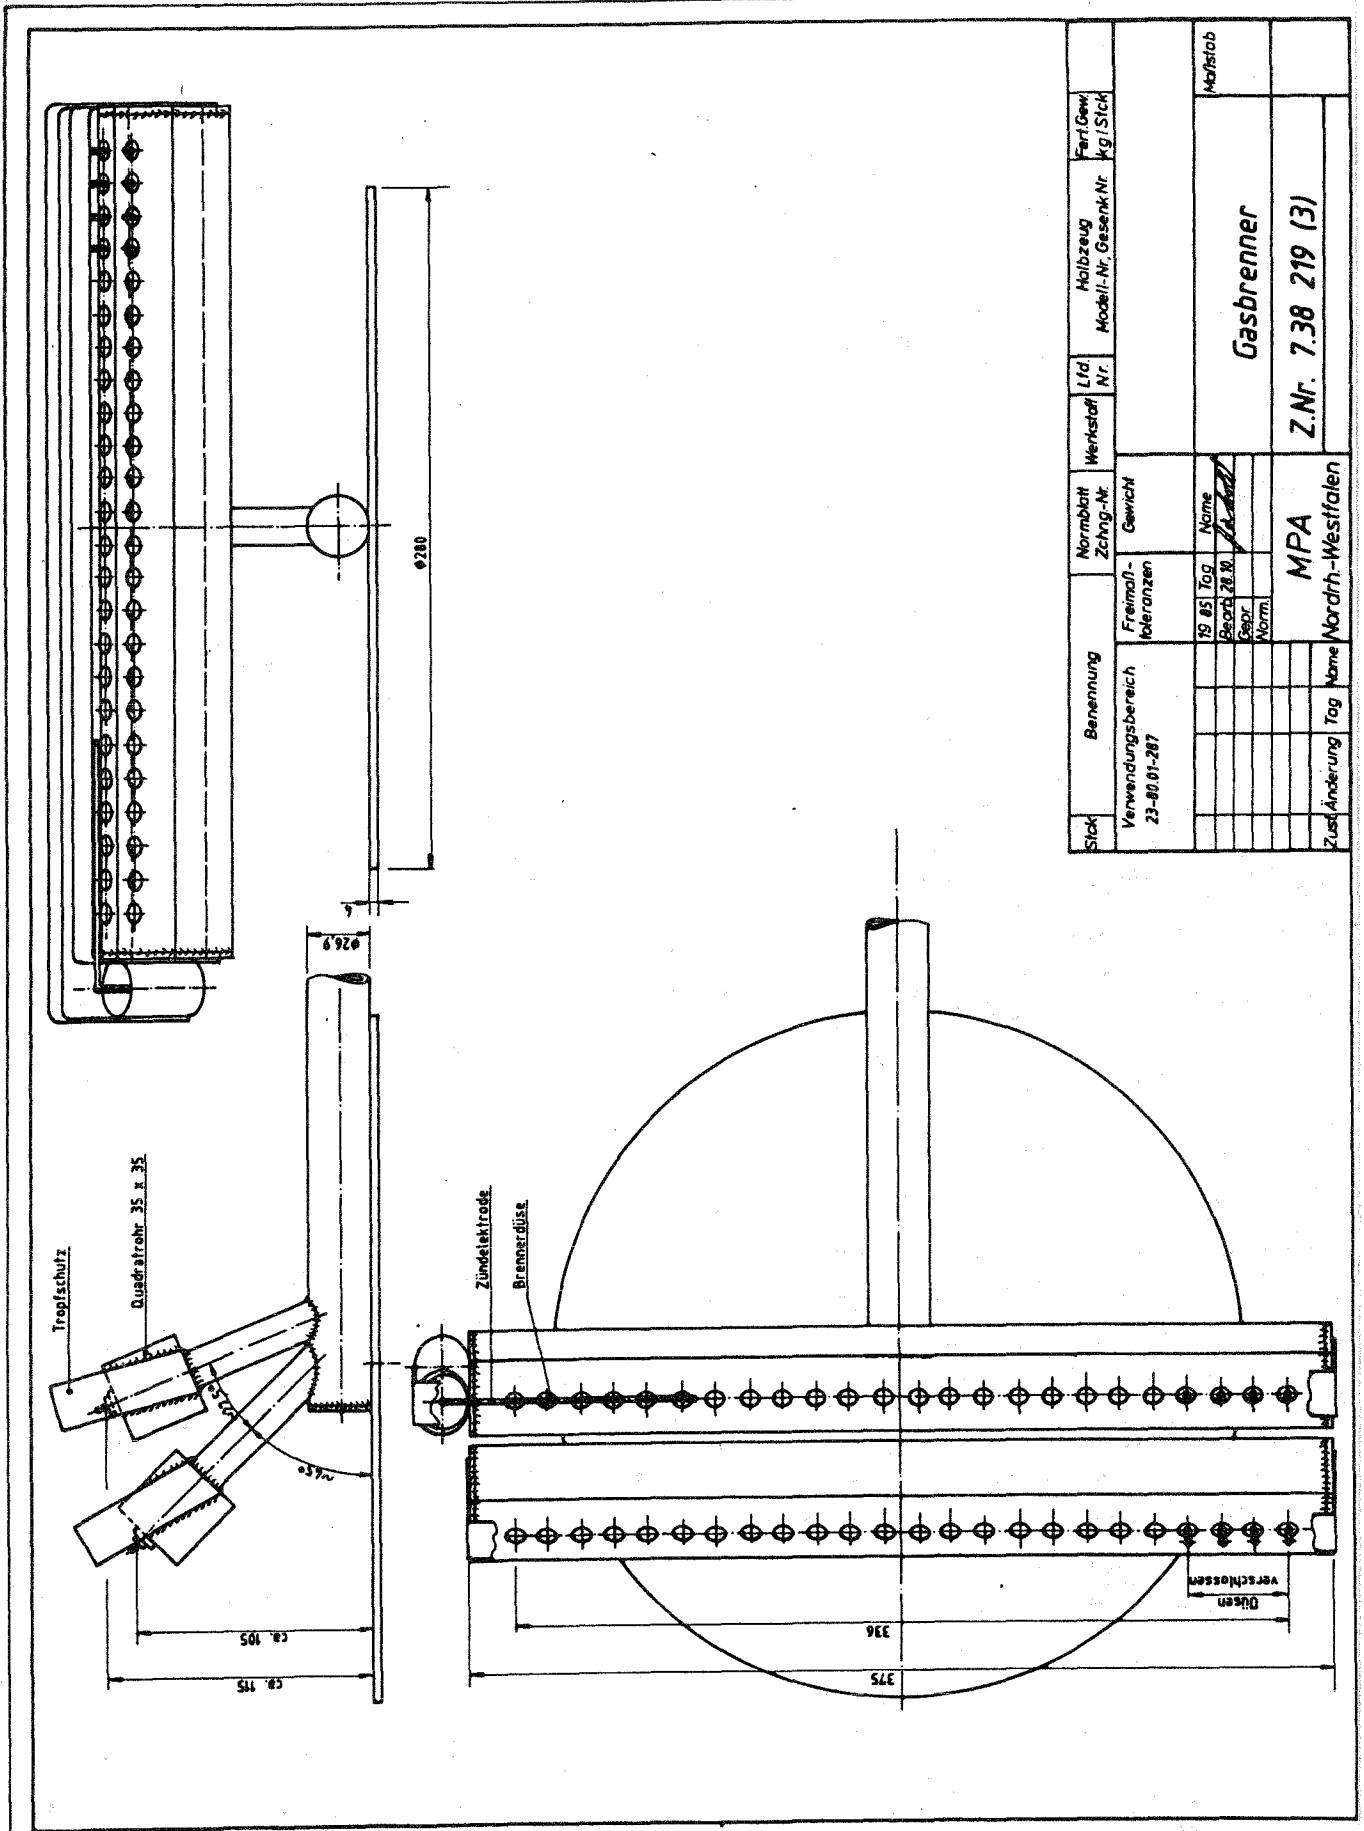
Gasbrenner - Seitenansicht und Draufsicht -
